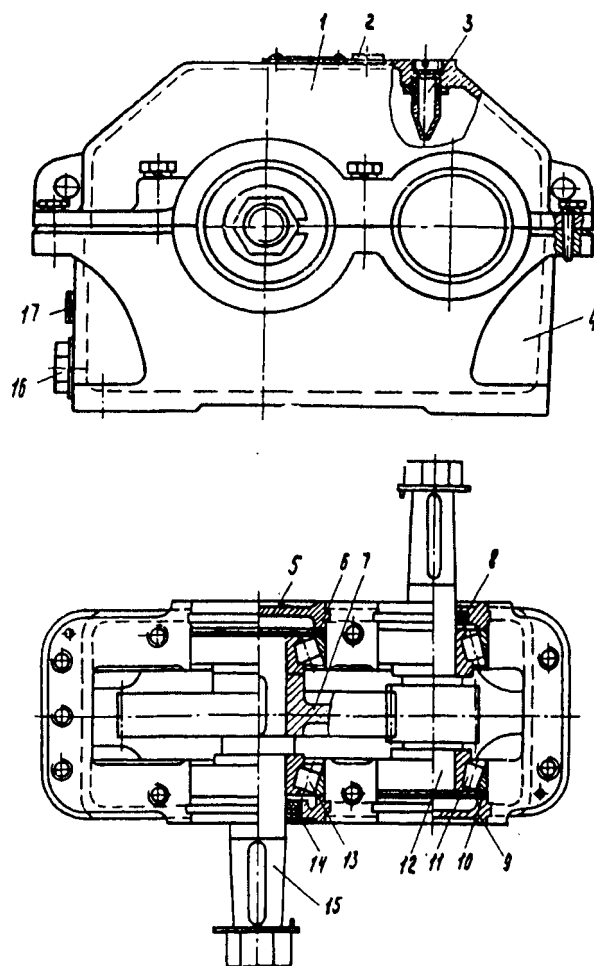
П7 Общий вид редукторов типа 1ЦУ
